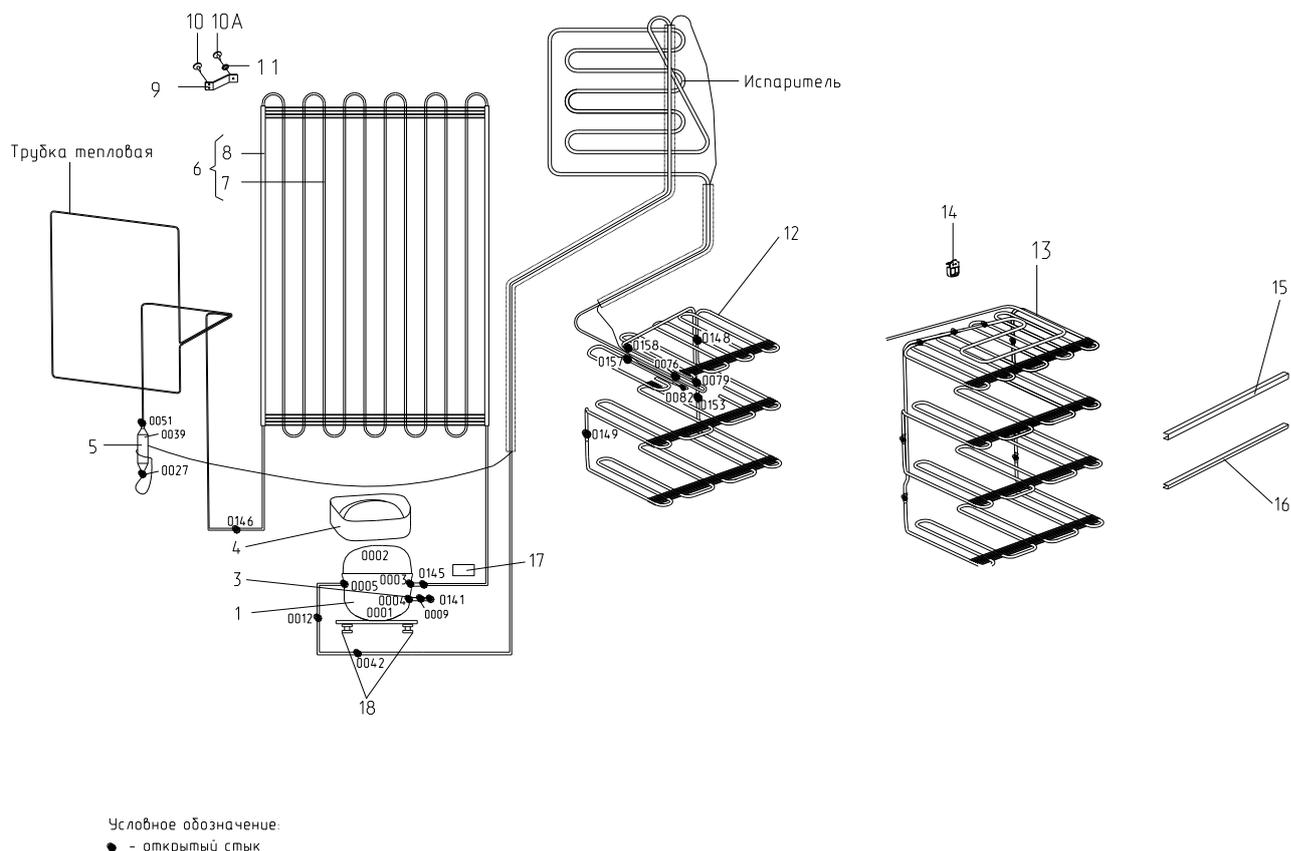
Схема холодильного агрегата (компрессор СТВ, СТС)
